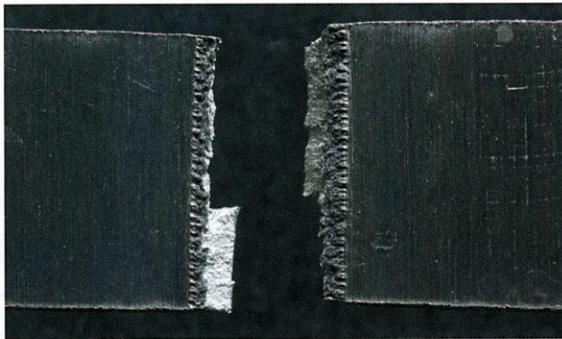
• Bruchbild der Zugprobe einer laserstrahlgeschweißten I-Naht am Stumpfstoß zweier Magnesiumbleche, Blechdicke 1mm, erreichte Zugfestigkeit 187 MPa.
